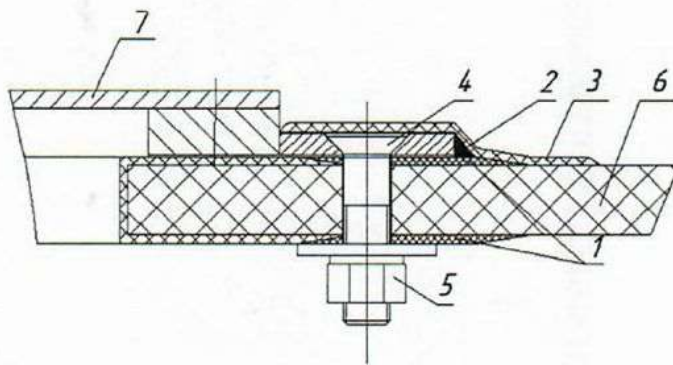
Вузол горловини з встановленою металевою кришкою: 1 - обформовка торця отвору; 2 – адгезійна речовина; 3 - приформовка; 4 - гвинт; 5 - гайка; 6 - обшивка цистерни; 7 - металева кришка
